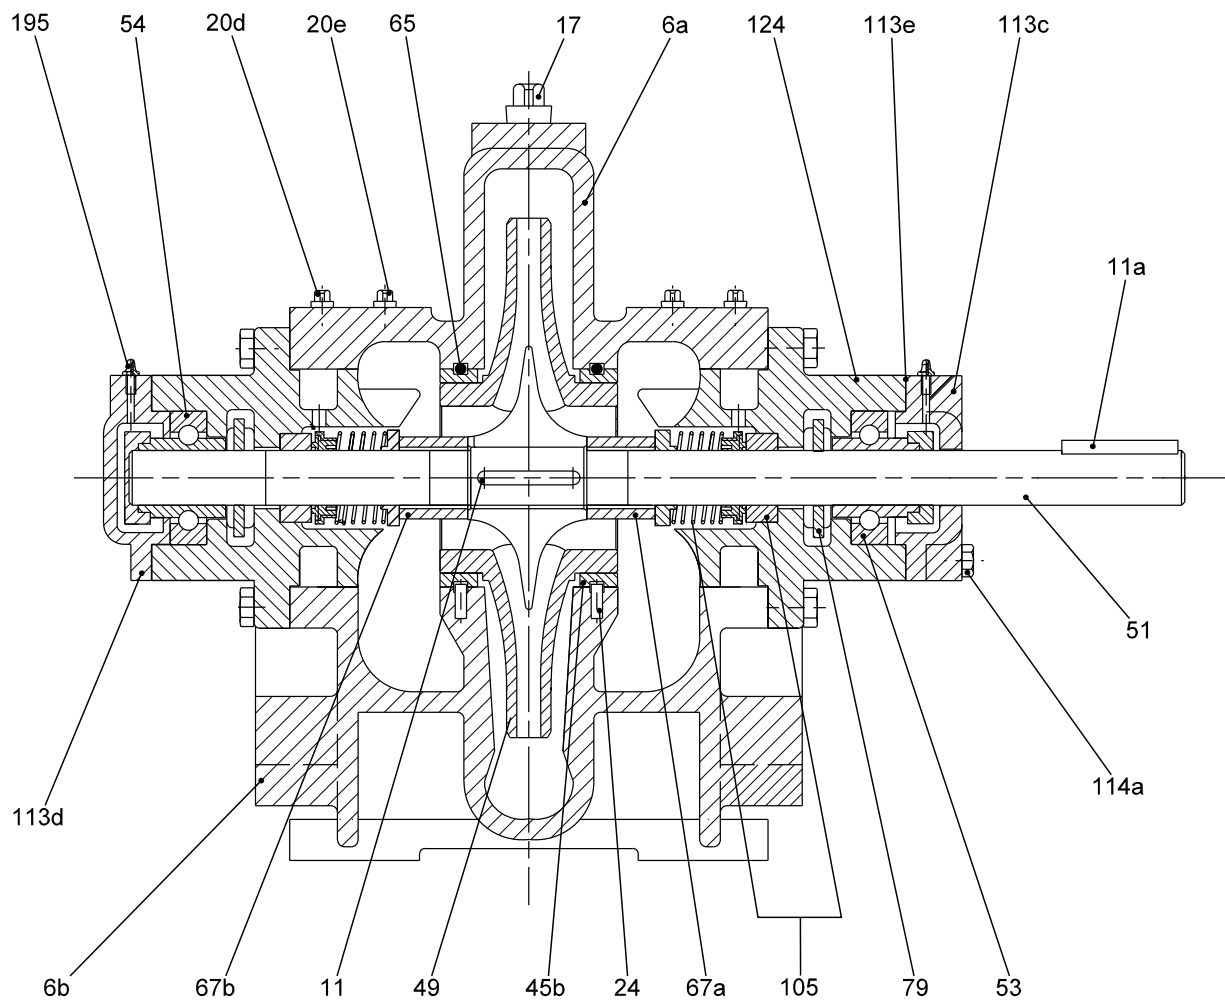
Sección, tipo de construcción 1, con cierres mecánicos del eje
